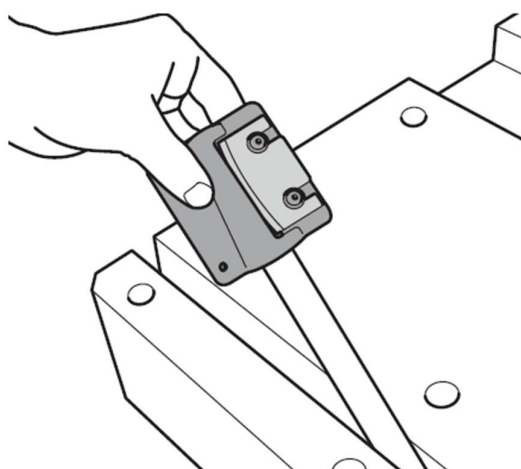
Verwendung eines Schraubstocks, Werkzeug wird gedreht
